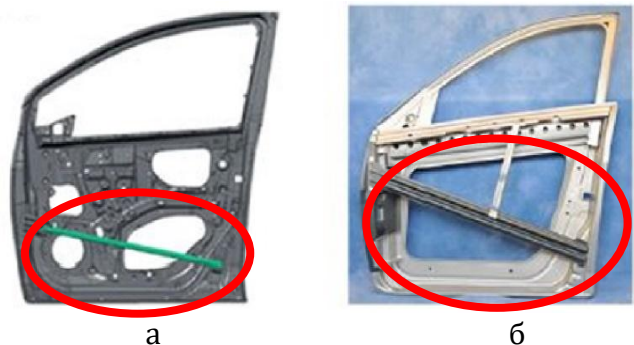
Види балок безпеки, що розташовані у дверях автомобіля [9]: а – балка круглого профілю; б – формована балка з листового металу
